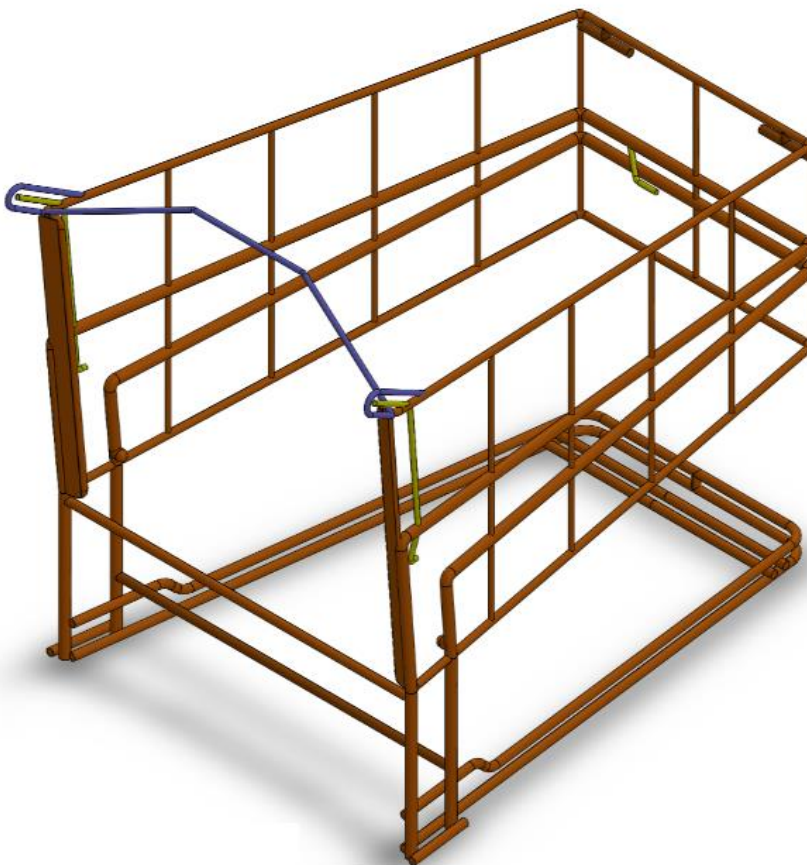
Vista de la cesta externa o revestimiento protector.
